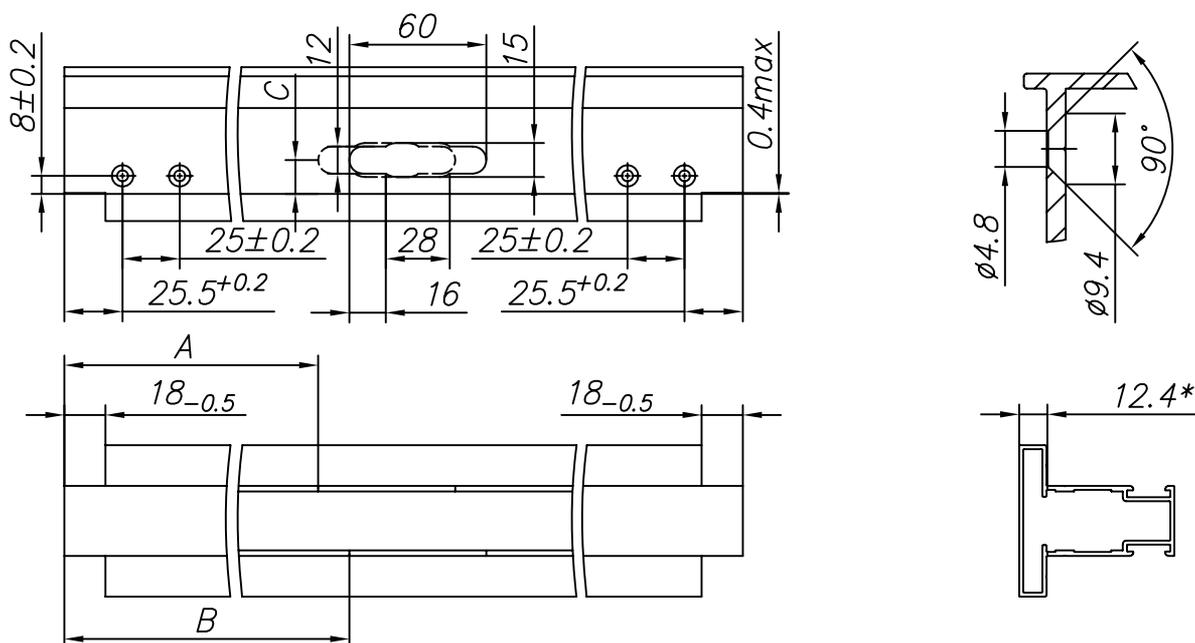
Изготовление импоста с пазами для тросовой растяжки
